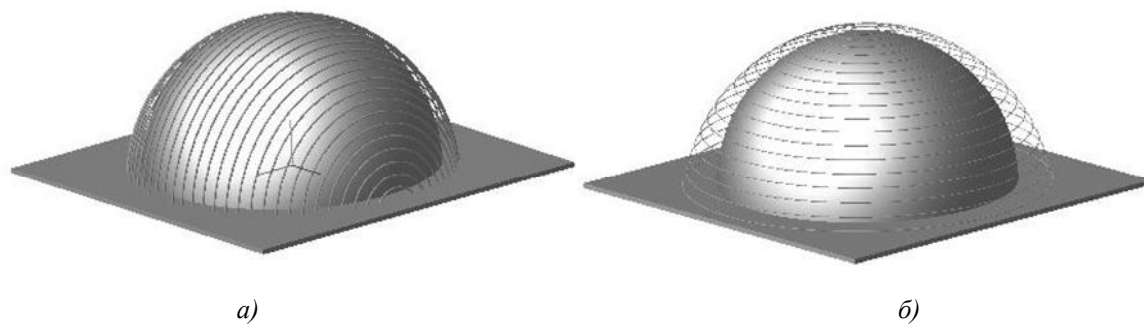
Стратегії обробки при фрезеруванні сферичних поверхонь
